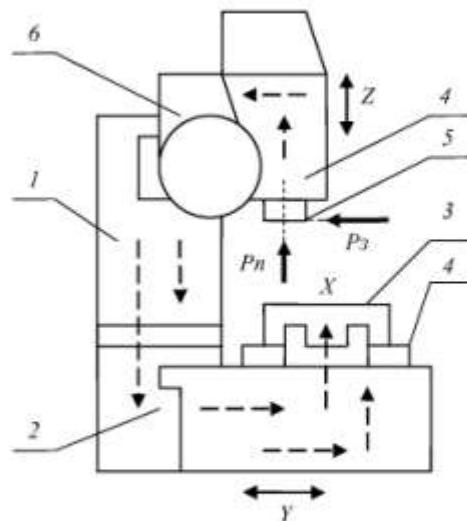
Схематичное расположение основных частей обрабатывающего центра
